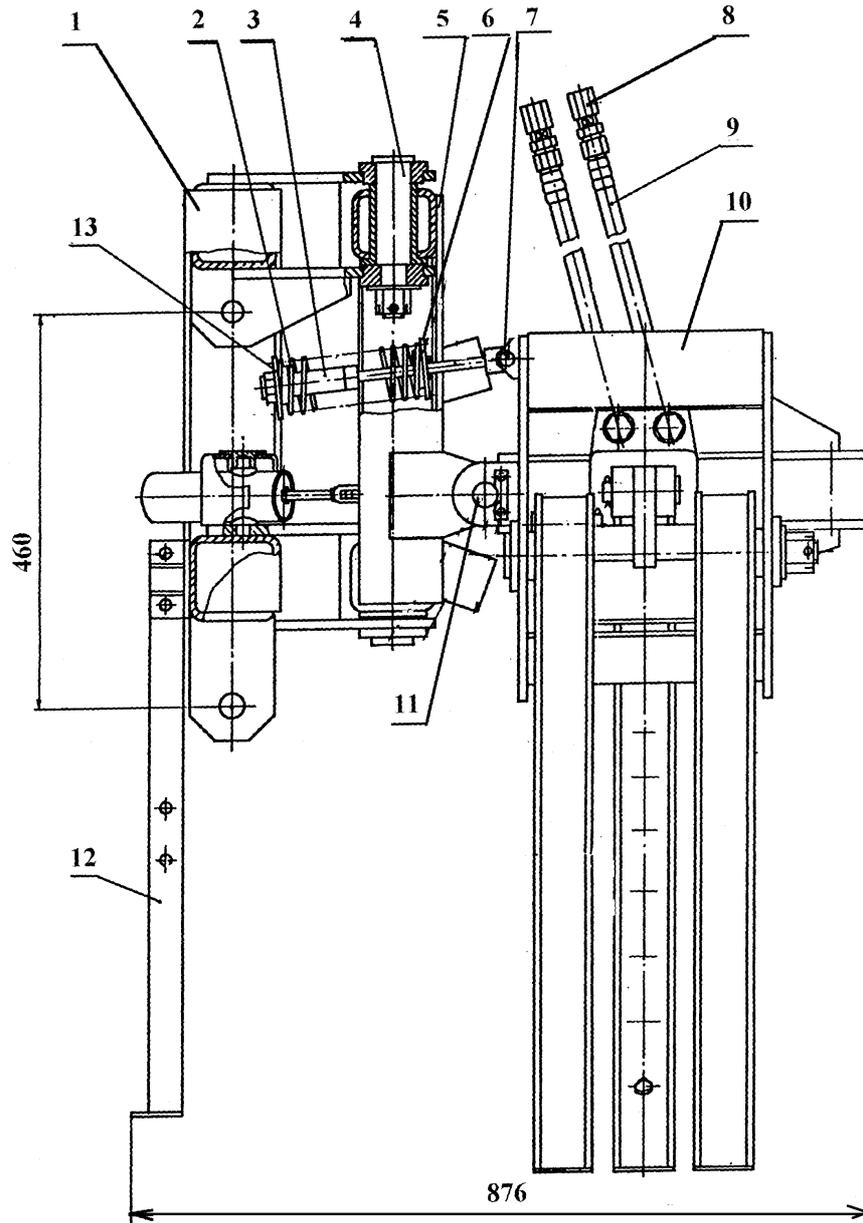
Трелевочный захват: 1 – звено навесное; 2 – пружина; 3 – стяжка; 4, 7, 11 – пальцы; 5 – крестовина; 6 – опора; 8 – клапан запорного устройства правый; 9 – шланг; 10 – корпус захвата; 12 – опора; 13 – тарелка
